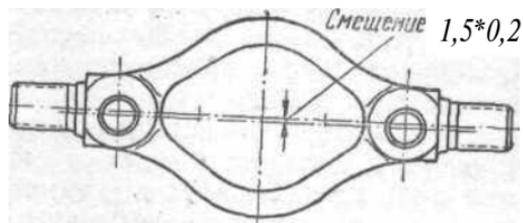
Ось верхнего рычага передней подвески автомобиля модели 407
